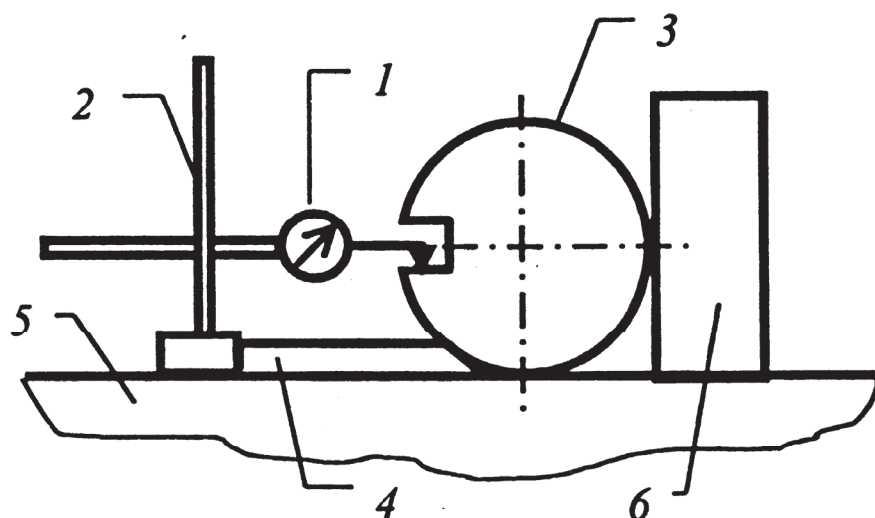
Схема приспособления для контроля перекаса шпоночного паза
